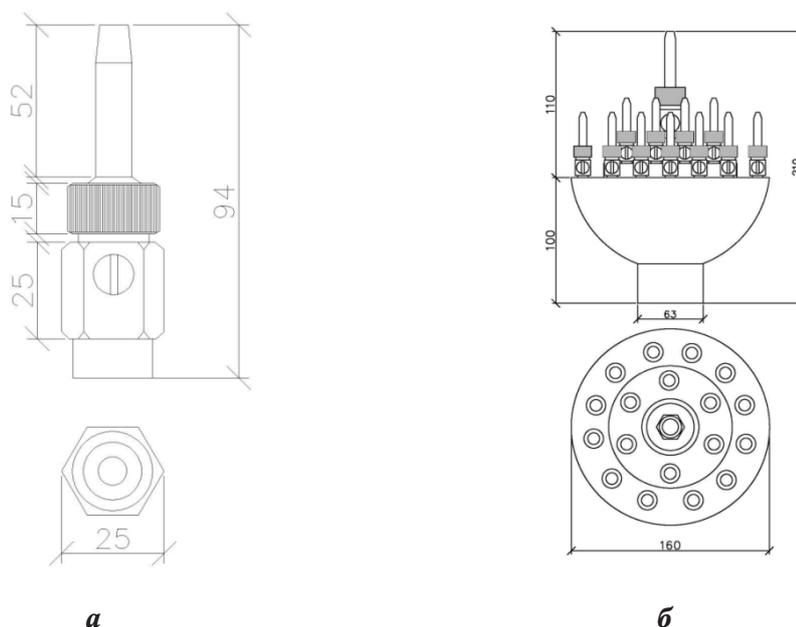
Конструктивная схема фонтанных насадок: а – «Комета»; б – «Феерия»
